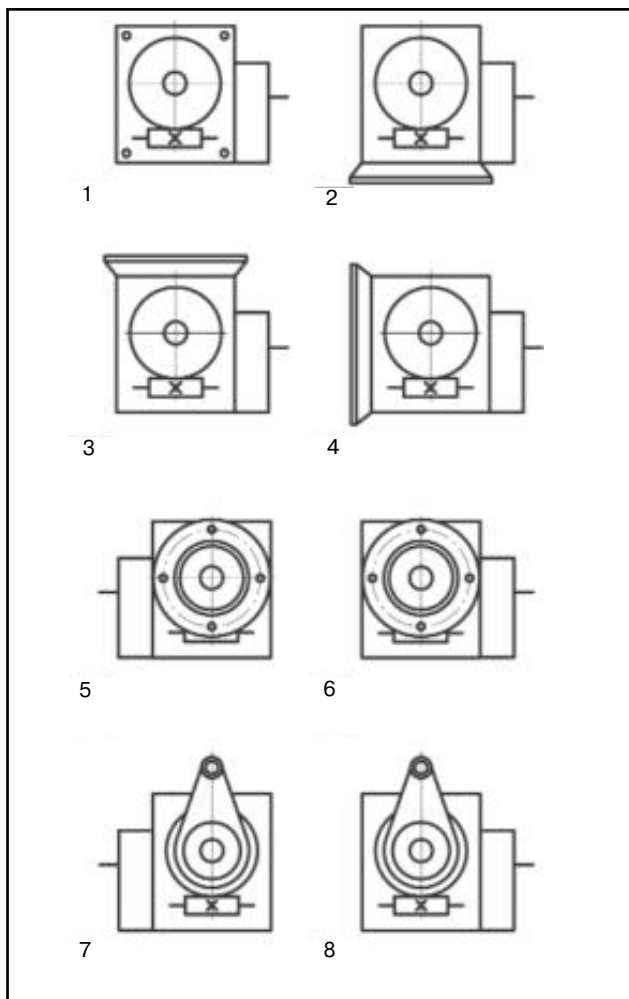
Варианты конструктивных исполнений по способу монтажа цилиндрично-червячных редукторов (мотор-редукторов):
